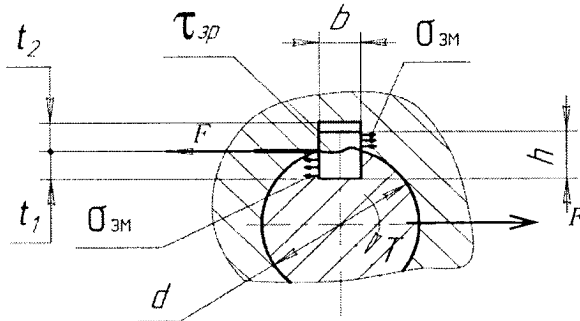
Розрахункова схема шпонкового з'єднання
